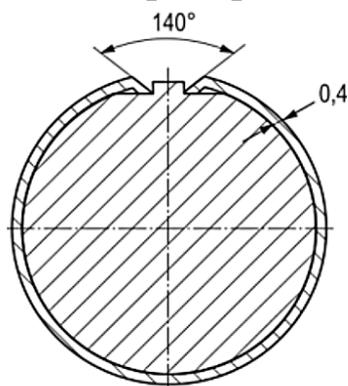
Схема установки упругой ДРД на шейку вала
